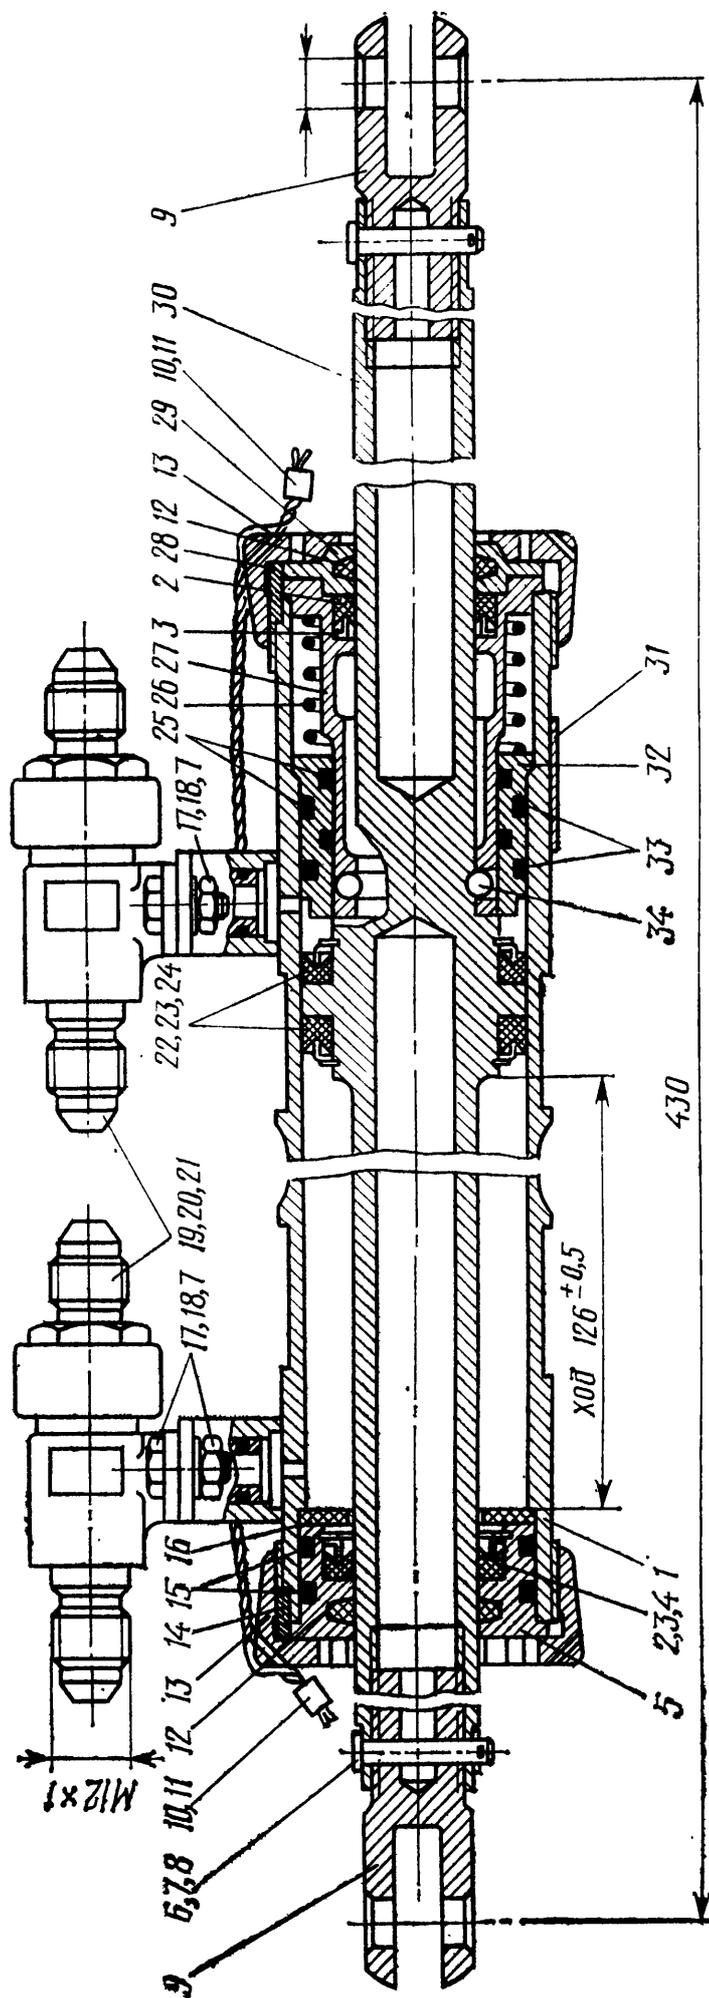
Цилиндр выпуска-уборки посадочных щитков:
